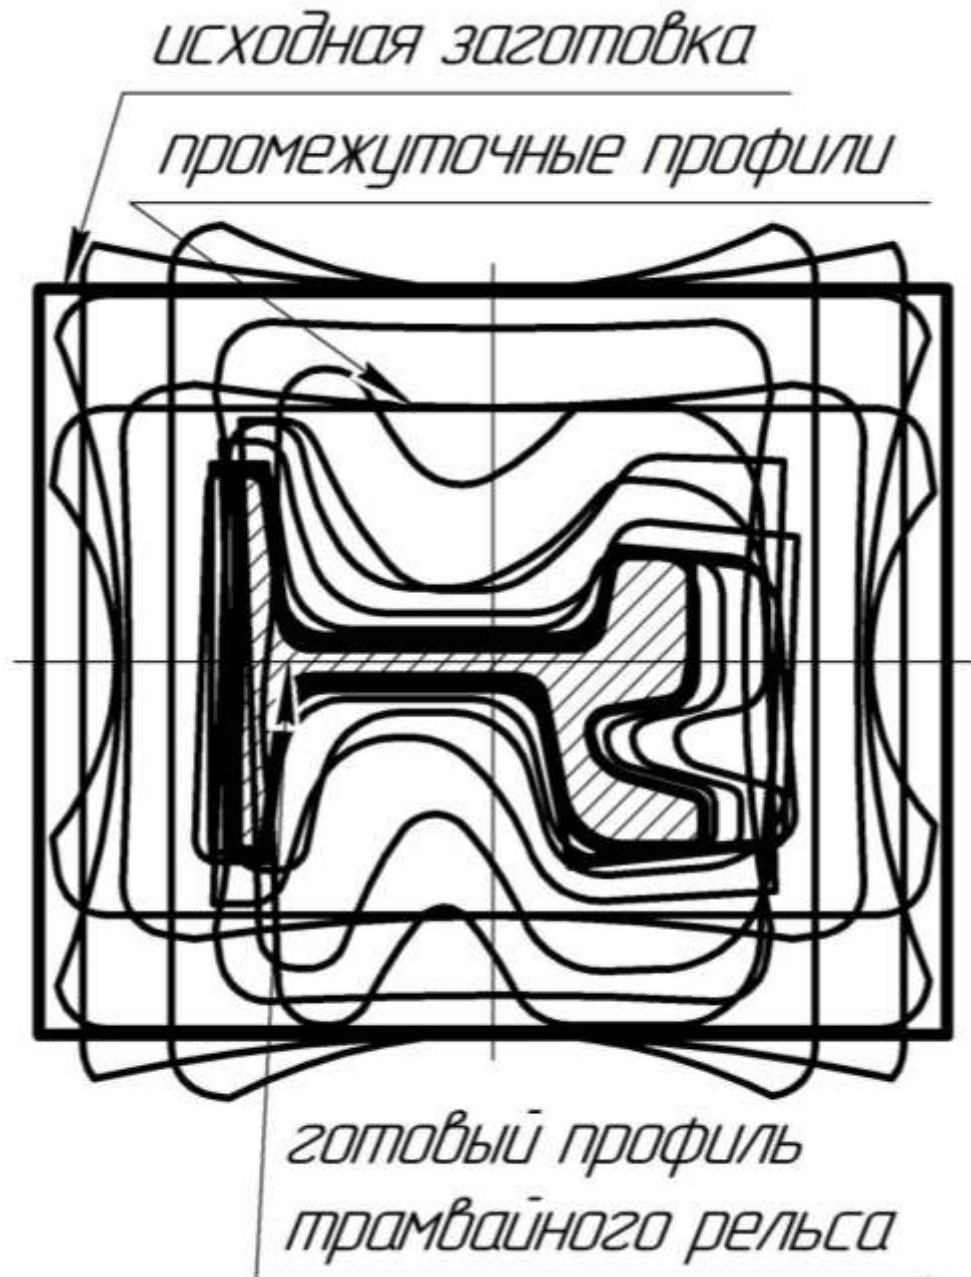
Схема деформации заготовки в готовый профиль
